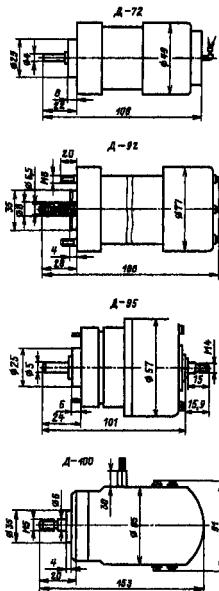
Габаритные и установочные размеры двигателей Д-72, Д-92, Д-95, Д-100
